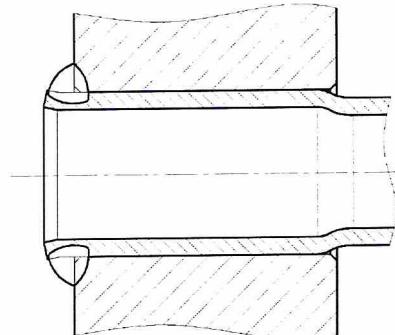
Развальцовка трубы по сварному шву.
